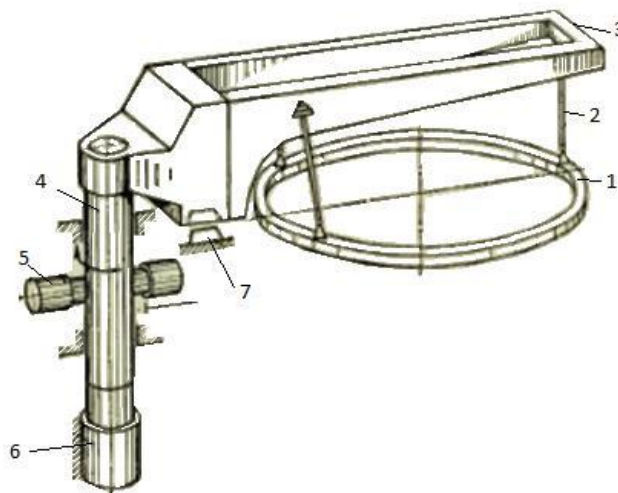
Механизм подъема и поворота свода: 1 – свод; 2 – подвеска; 3 – кронштейн; 4 – опорно-поворотный вал; 5 – гидроцилиндры поворота; 6 – гидроцилиндр подъема; 7 – фиксатор
